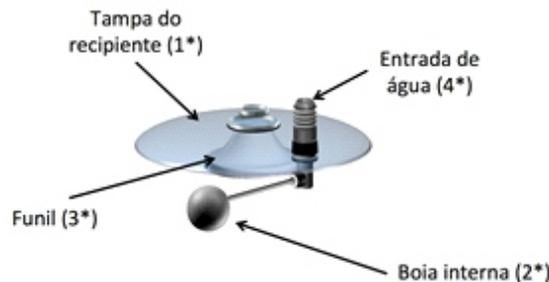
Tampa da bombona com boia e funil (3*) instalada e posicionado.
